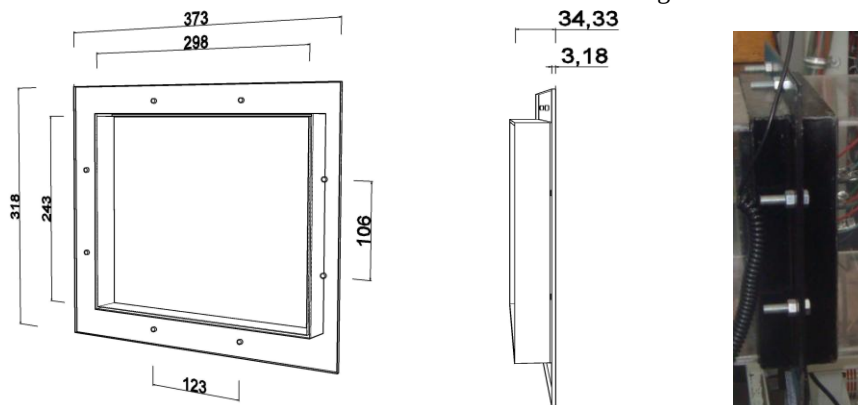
Brida para la unión de las tres secciones del túnel (acotaciones en mm).
